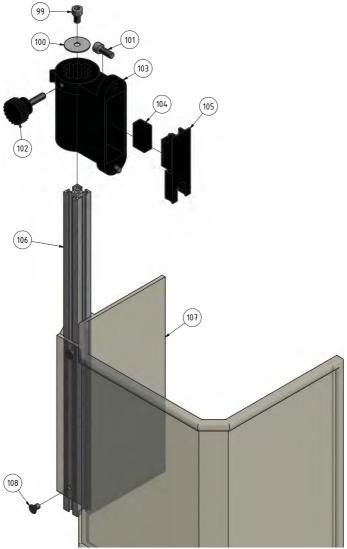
Bohrfutterschutz- Drilling chuck protection
